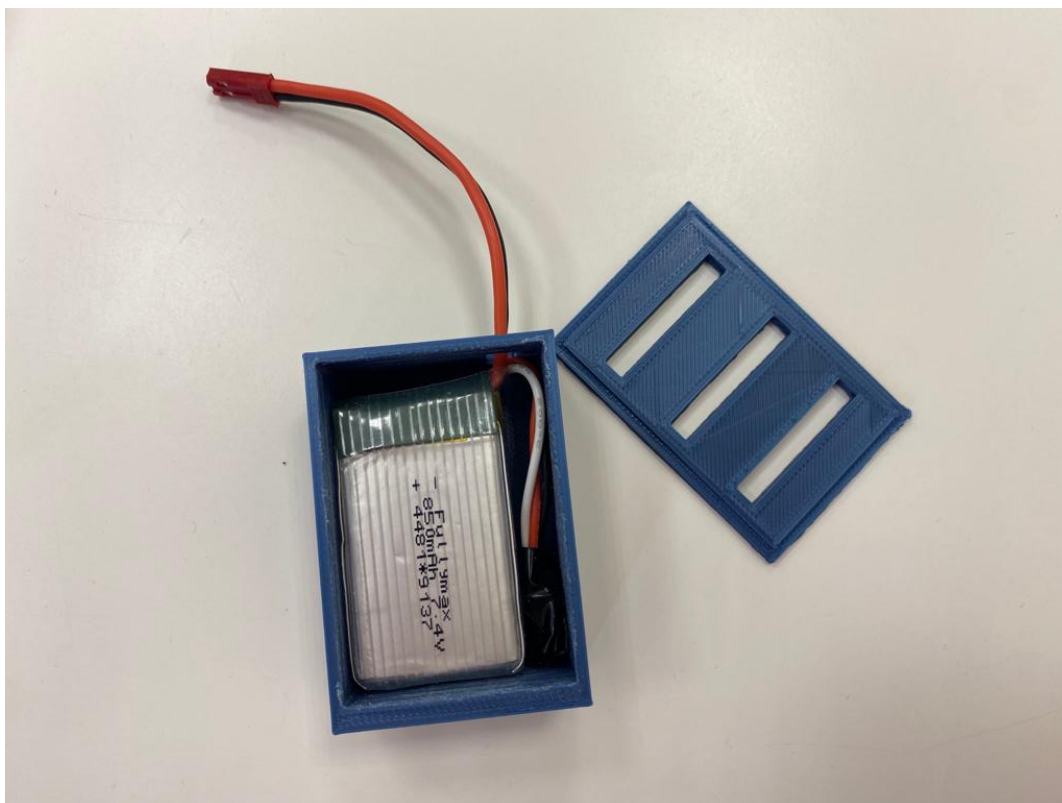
Корпус для аккумулятора, напечатанный на 3Д-принтере
